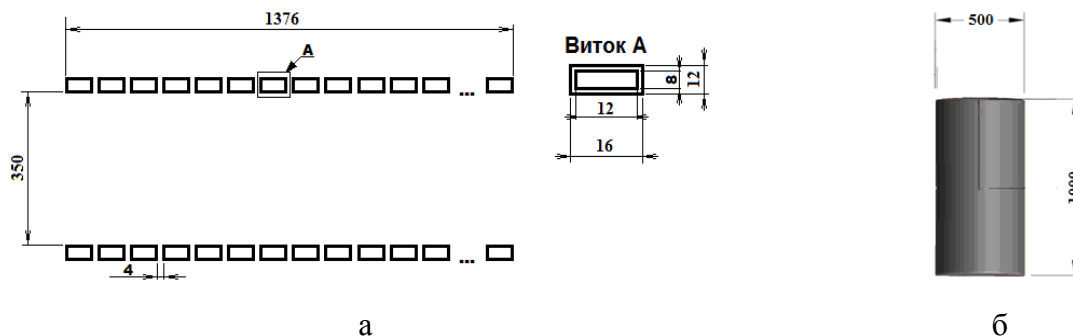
Конструктивные параметры индуктора и заготовки (в мм):
